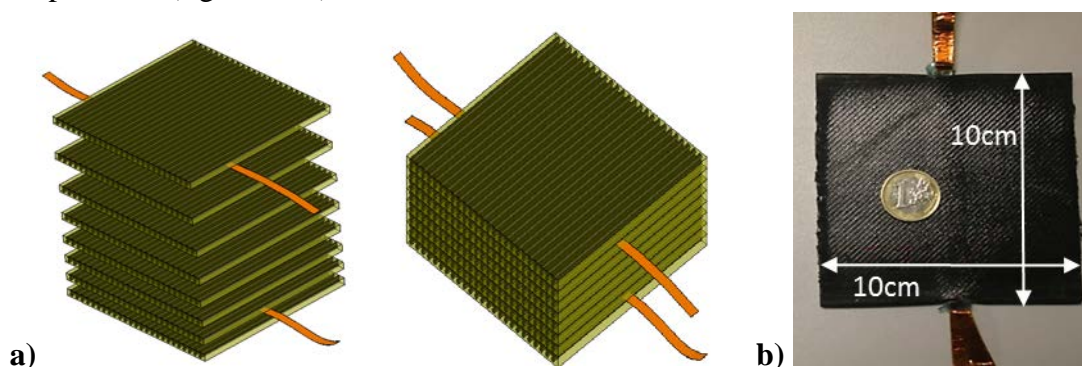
a) le plan et b) la photo de la plateforme d'instrumentation transversale inter-ply (8 plis)
